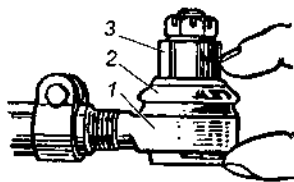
Проверка зазоров шарниров рулевых тяг на автомобилях классической компоновки: 1 — наконечник рулевой тяги; 2 — защитный чехол; 3 — рычаг
